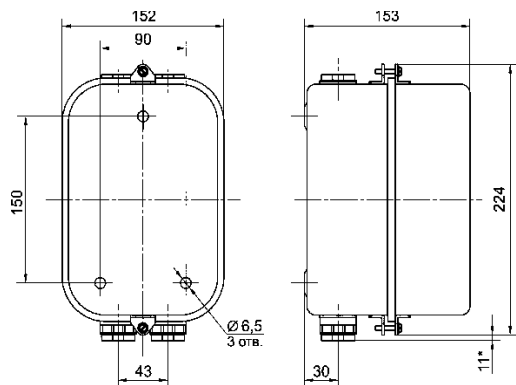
Пускатель ПМ12-040 40А в защитном корпусе - IP40; IP54
